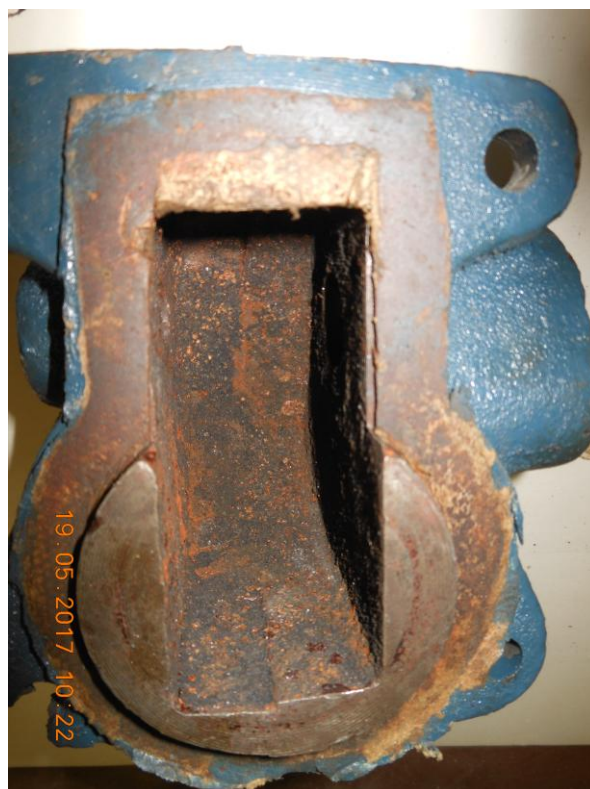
Осмотр сопрягаемых поверхностей корпуса насоса и корпуса привода поршня
